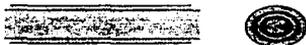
Empaquetadura Tejida Capa Sobre Capa
